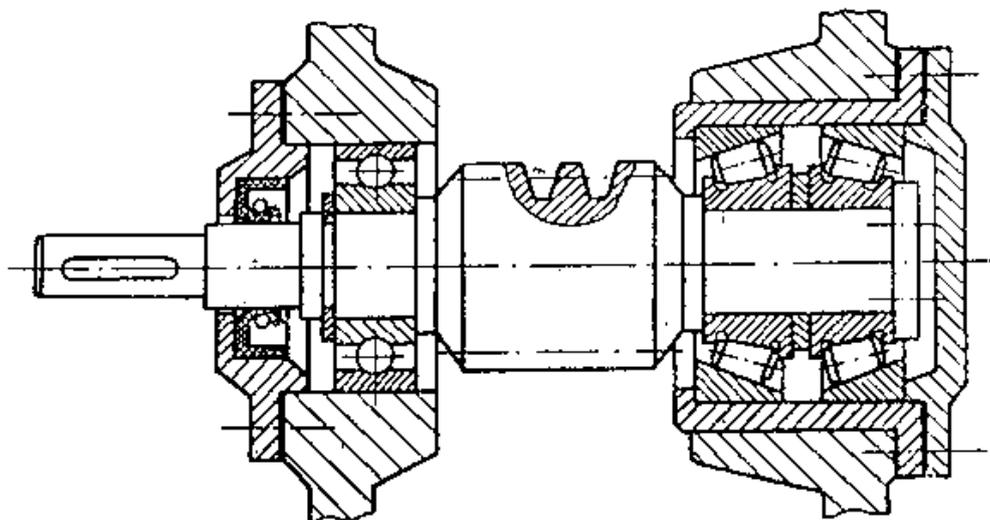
Пример конструкции подшипниковых узлов с плавающей опорой
